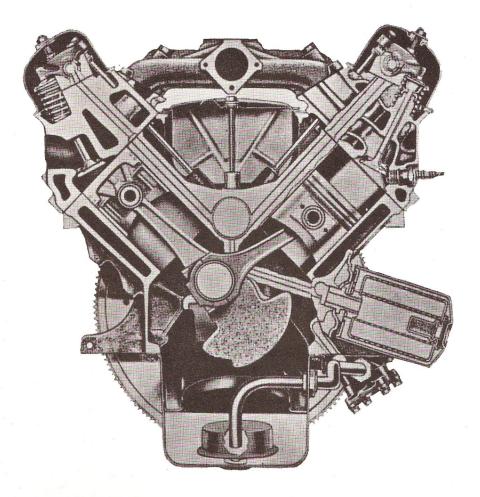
Vista Seccional del Motor V-8 292. Típica.
